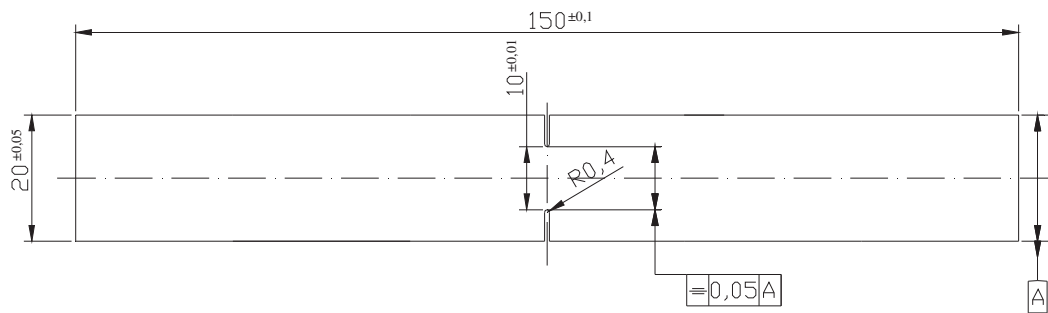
Eprouvette plate entaillée ($R = 0,4$ mm ; épaisseur = 3 mm).
